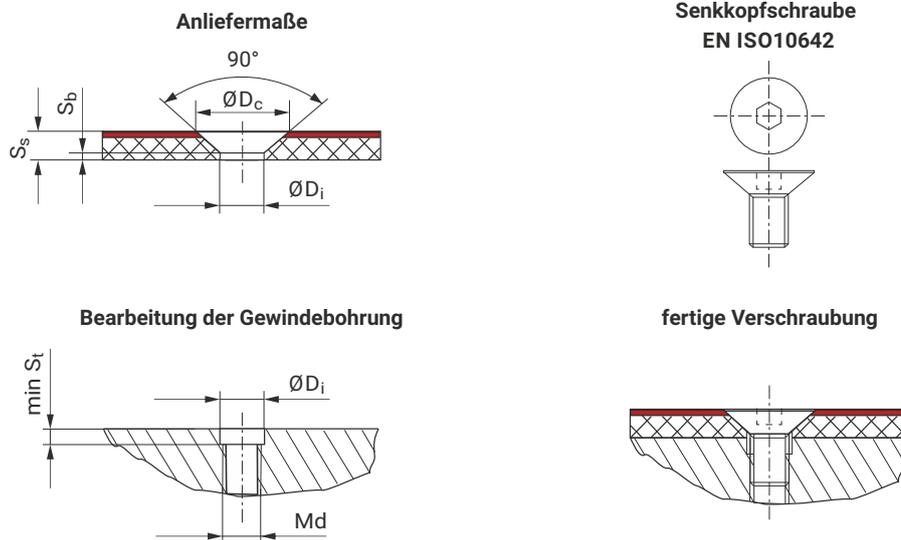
Gleitplattenbefestigung mit Senkkopfschrauben
